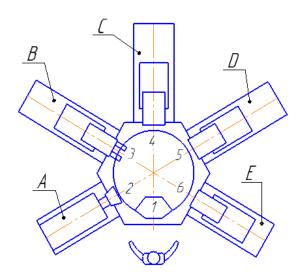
Агрегатный станок с поворотным столом "Cross"
